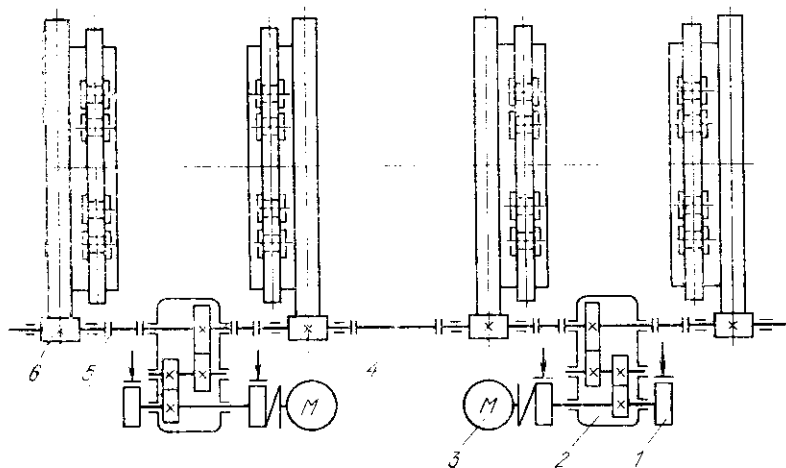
Кинематическая схема механизма поворота ротора стационарного роторного вагонопрокидывателя:
